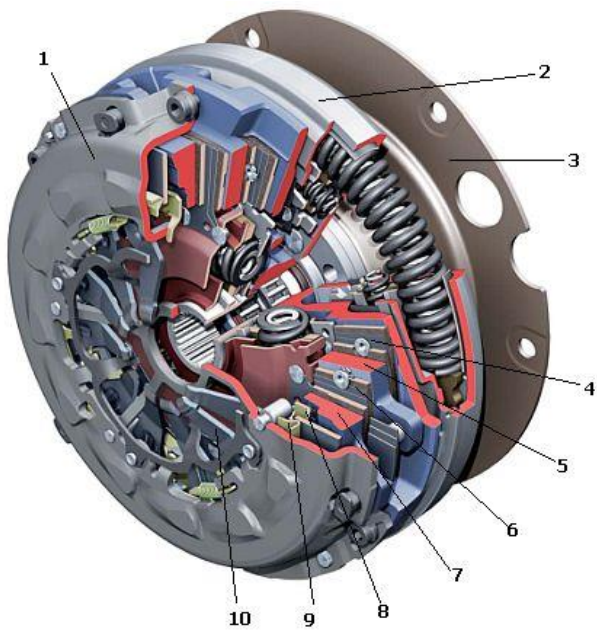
Схема двухдискового сцепления [6]: 1 – крышка корпуса; 2 – двухмассовый маховик; 3 – приводная пластина; 4 – ведомый диск 2 с демпферными пружинами; 5 – проставка; 6 – ведомый диск 1; 7 – нажимной диск; 8 – сенсорная пружина; 9 – регулировочное кольцо; 10 – диафрагменная пружина
